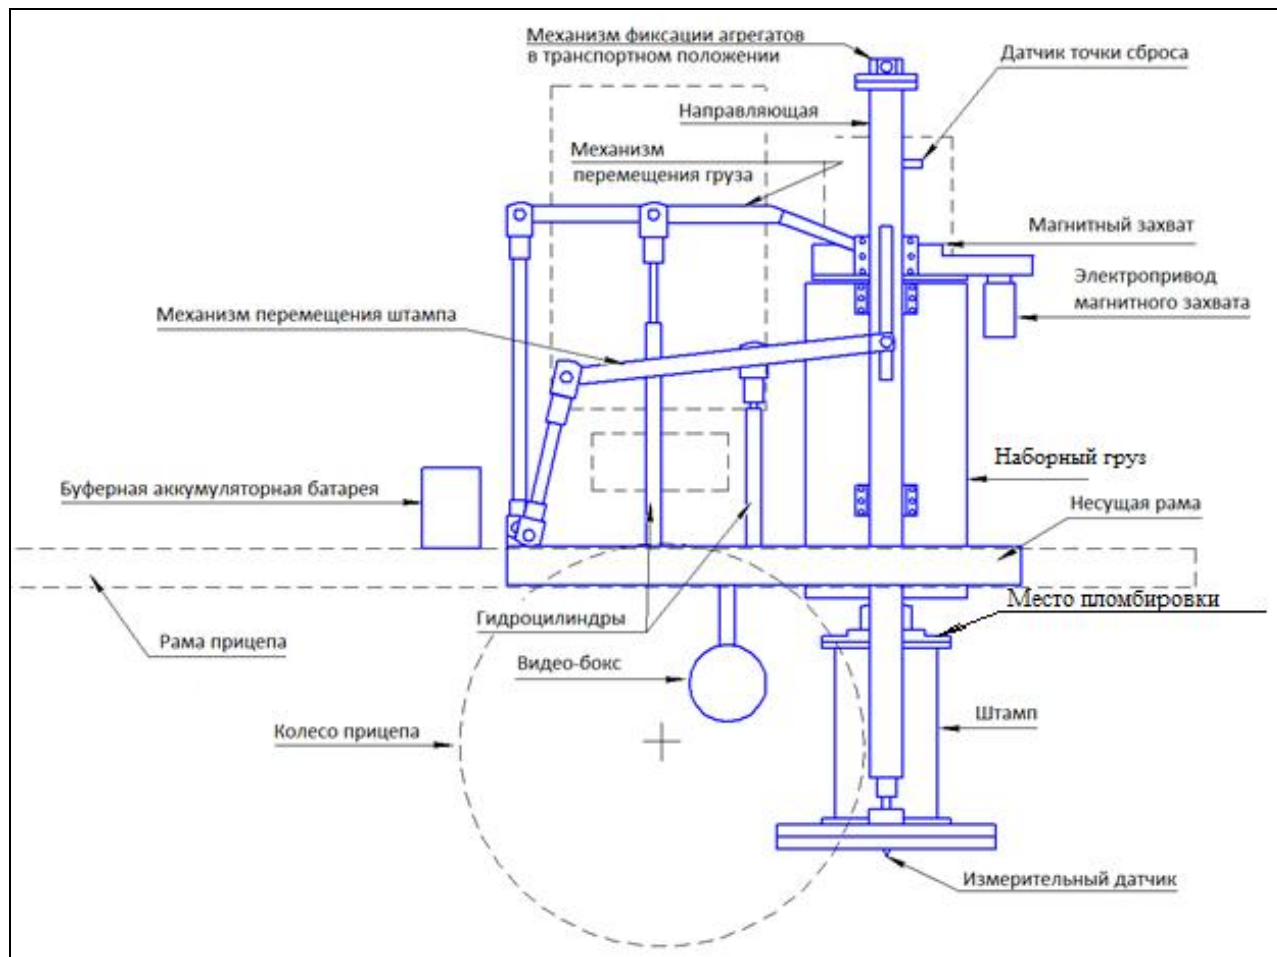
Схематичное устройство измерителей (вид слева)
